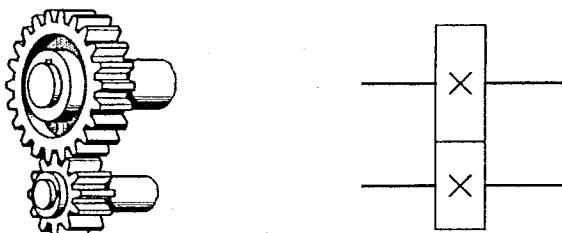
Циліндрична зубчаста передача (*toothed transmission*)
